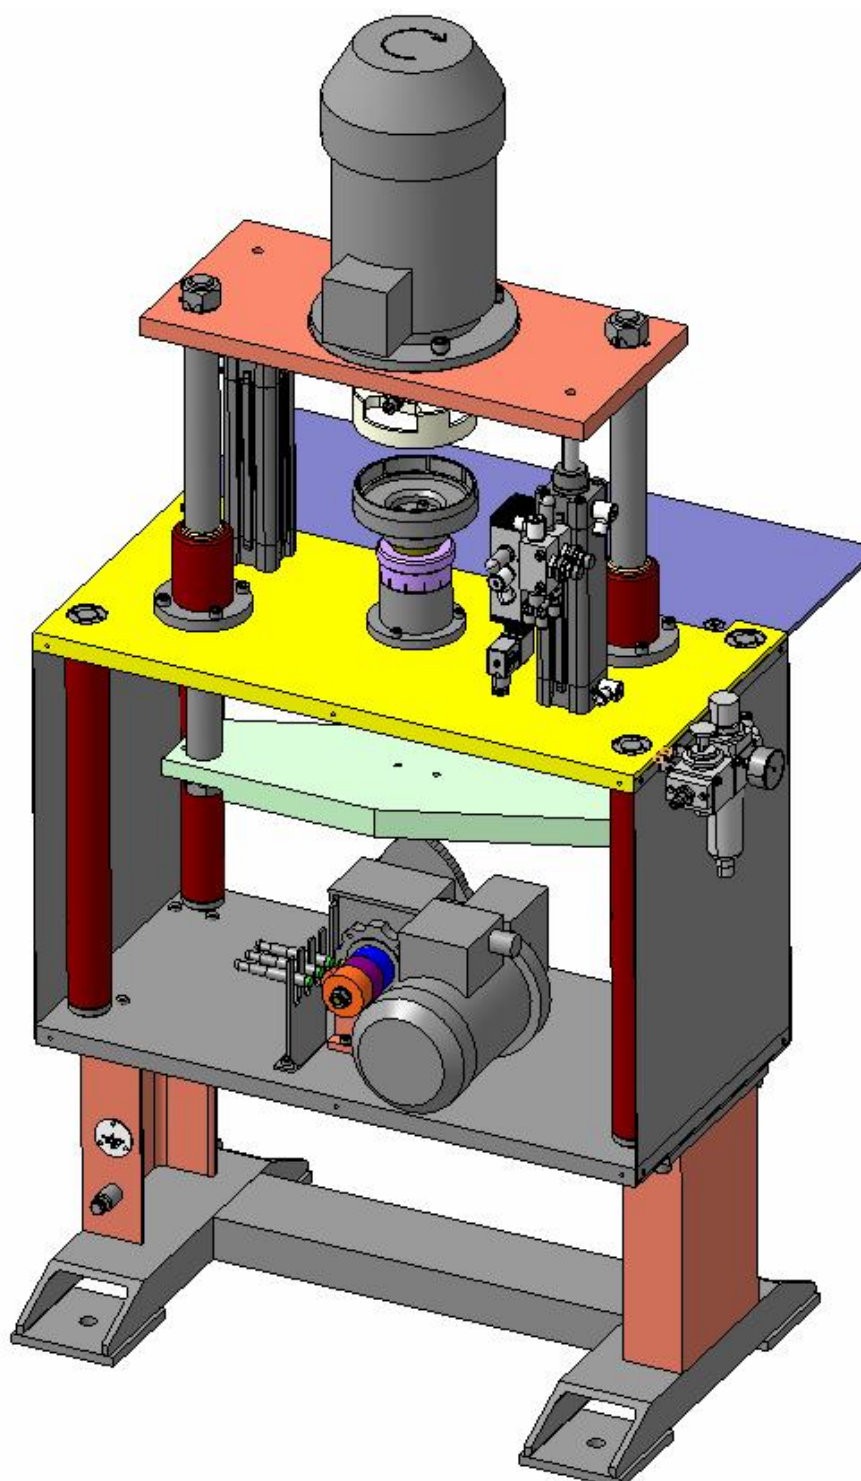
3D-вид модели *технологического комплекса сварки трением
